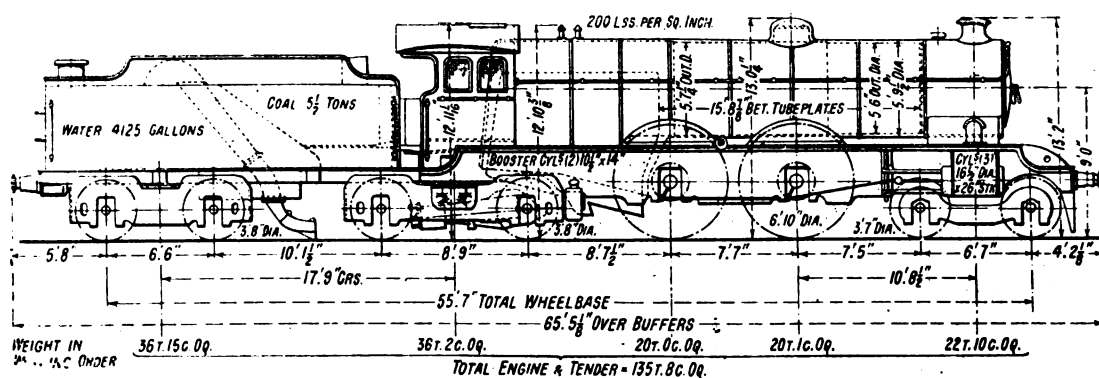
Vista generale e dimensioni principali della stessa locomotiva, modificata con l'aggiunta di un carrello e del booster, per la L. N. E. R.
